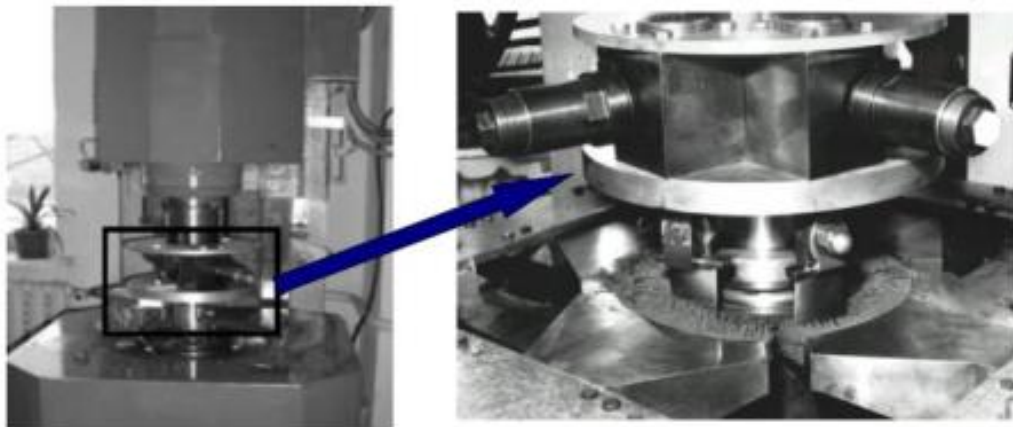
Зовнішній вигляд установки для МАО лопаток ГТД [67].
